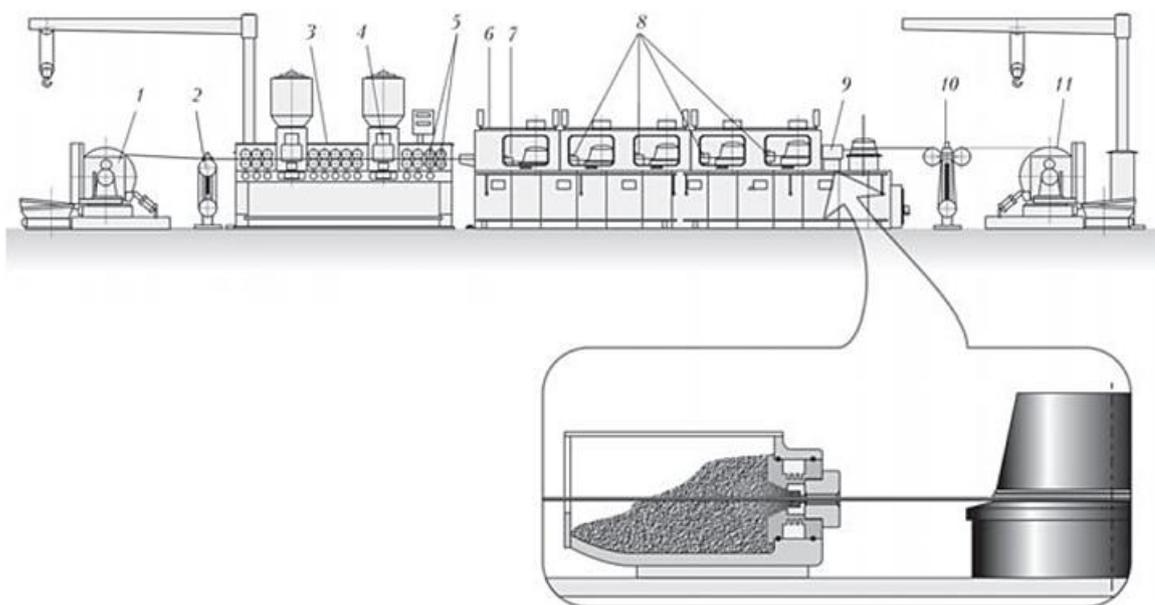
Линия изготовления сварочной порошковой проволоки: 1 – размоточное устройство для ленты; 2 – демпфер-регулятор натяжения ленты; 3 – формовочный агрегат; 4 – дозатор шихты; 5 – два дополнительных блока роликового редуцирования заготовки проволоки; 6 – волочильный стан; 7 – блок первичного волочения заготовки проволоки; 8 – блоки промежуточного волочения; 9 – блок калибрующего волочения проволоки с системой нанесения протекторного покрытия; 10 – демпфер-регулятор натяжения проволоки; 11 – намоточный аппарат
